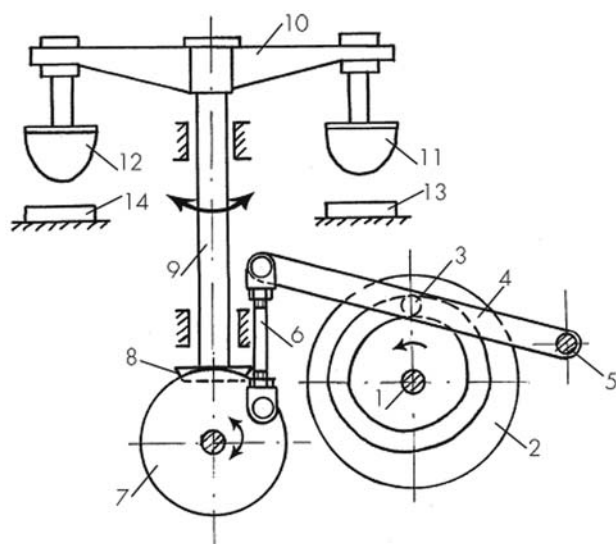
Механічний МПД фірми «Homer Laughlin China Company» (США)
